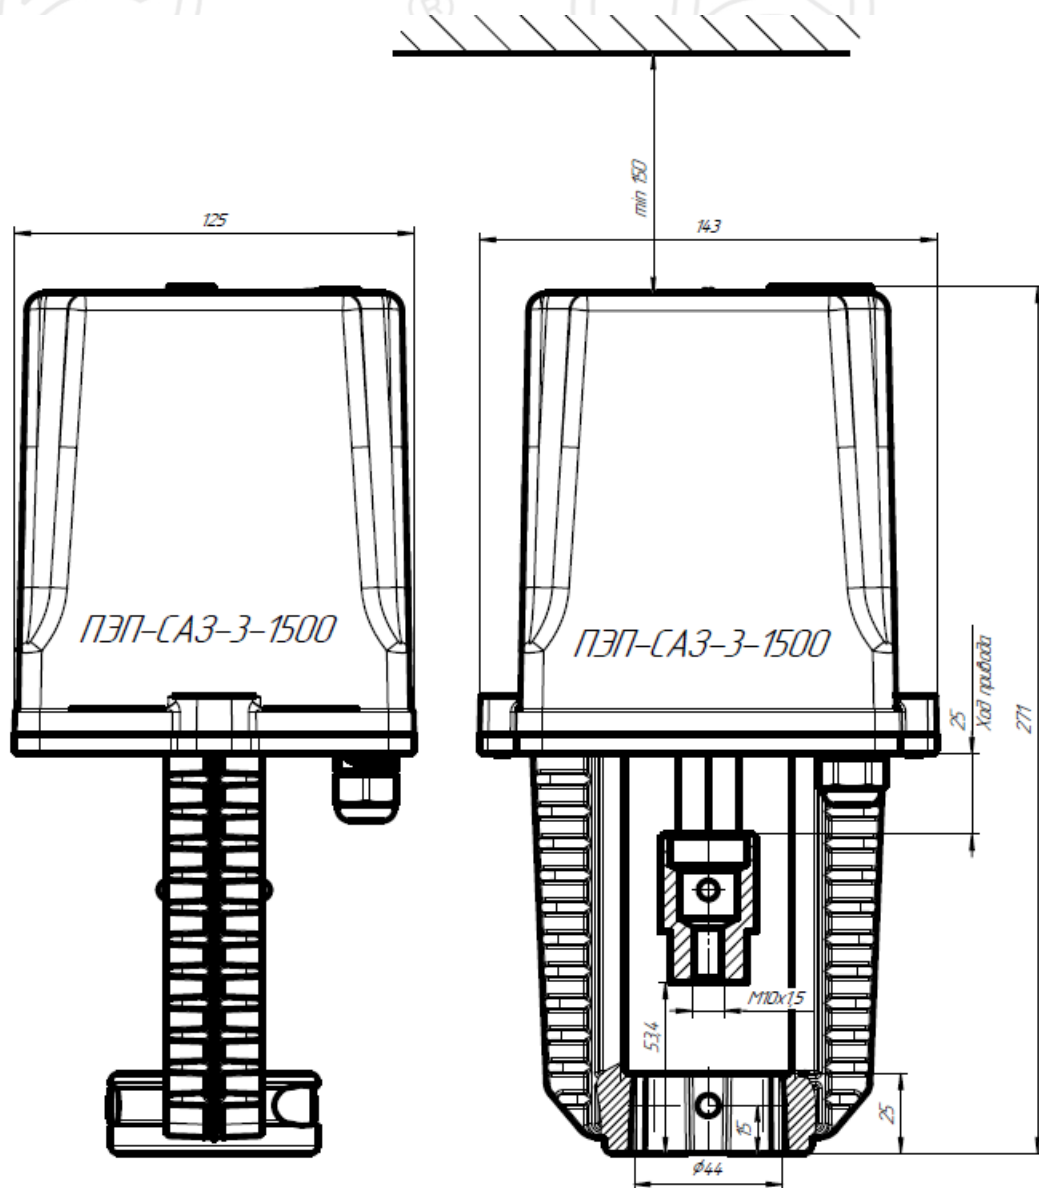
Габаритные и присоединительные размеры ПЭП-САЗ-3-1500
